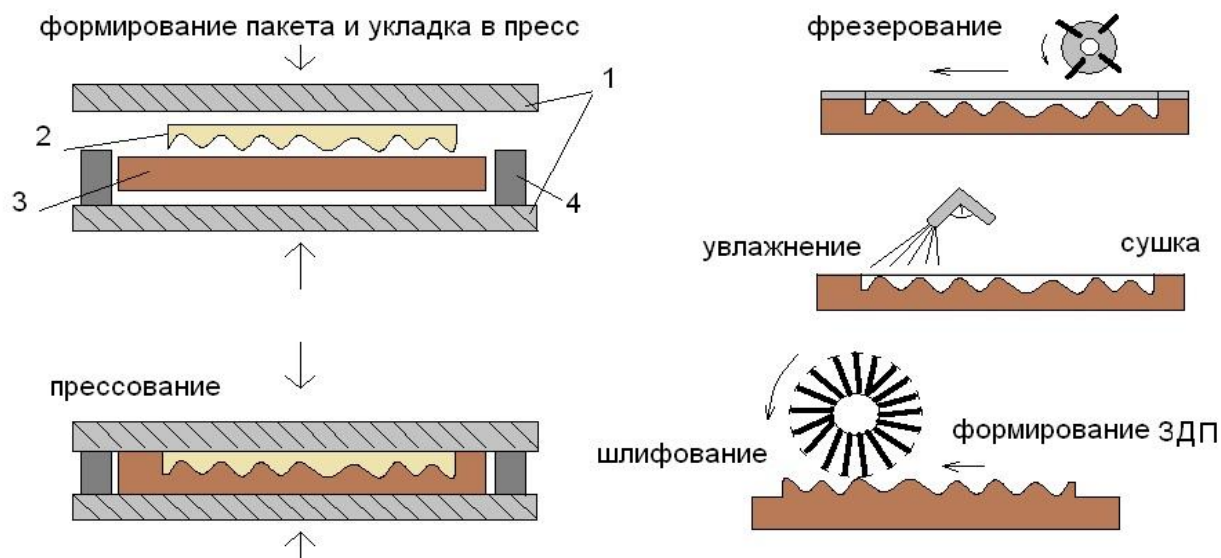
Схема технологического процесса формирования рельефного оттиска на поверхности детали из древесины: 1 – плиты пресса; 2 – пуансон; 3 – заготовленная деталь из древесины; 4 – стальные пластины
